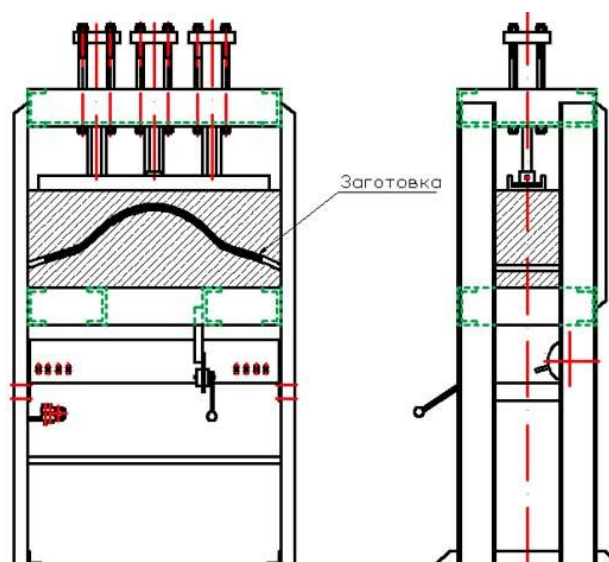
Обогреваемая пресс-форма для гнуто-клееных конструкций из древесины
